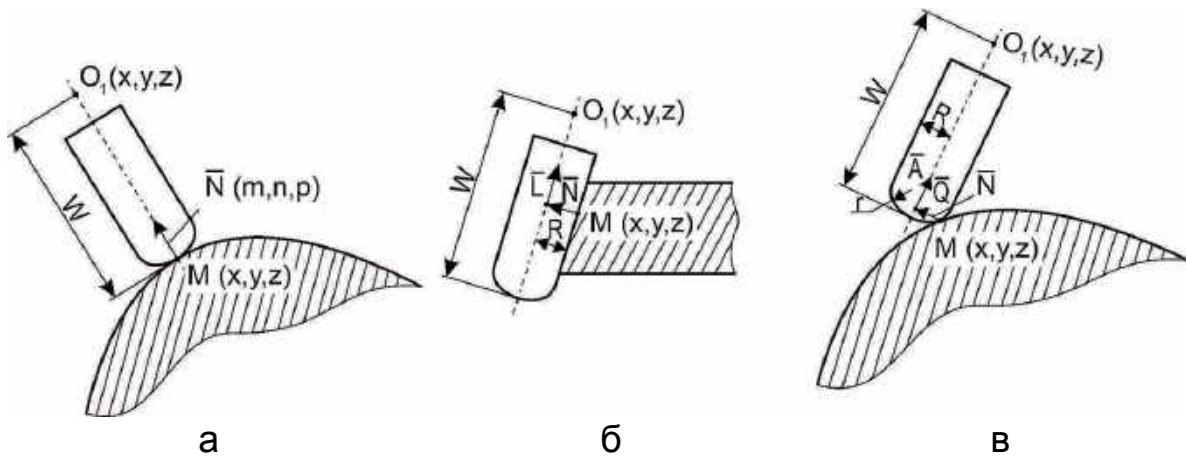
Основні види п'ятикоординатного фрезерування:
